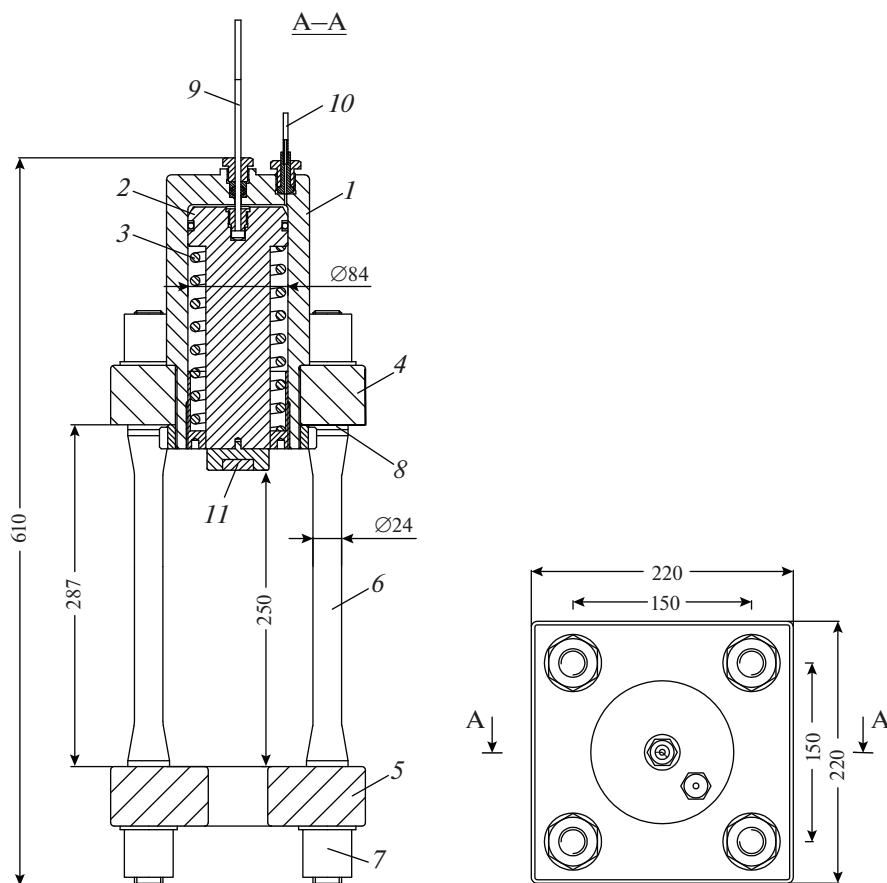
Общий вид лабораторного пресса. 1 – цилиндр; 2 – поршень; 3 – пружина обратного хода; 4 – верхняя плита; 5 – нижняя плита; 6 – колонны; 7 – гайки; 8 – подгоночные шайбы; 9 – индикатор перемещения поршня; 10 – вход для гидравлической жидкости; 11 – подпятник.
